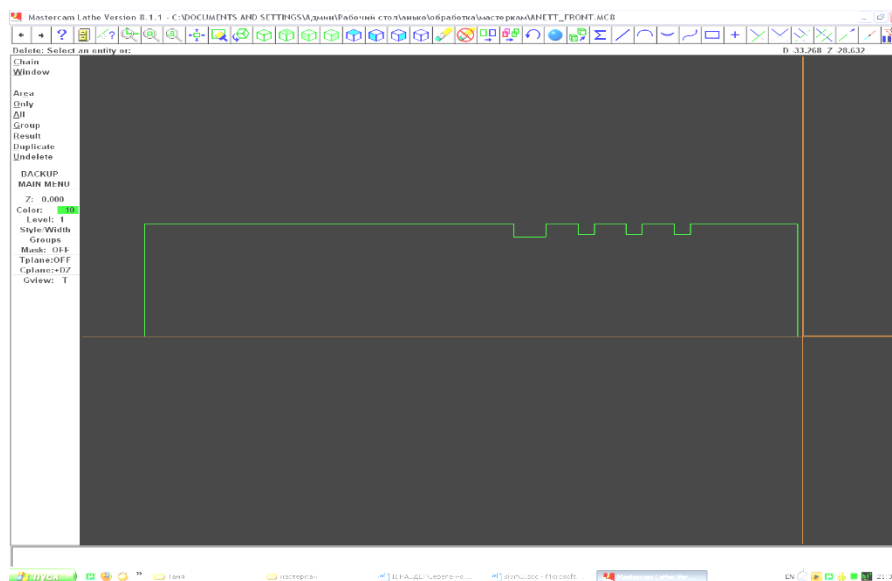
Імпортований ескіз контуру поверхні деталі
